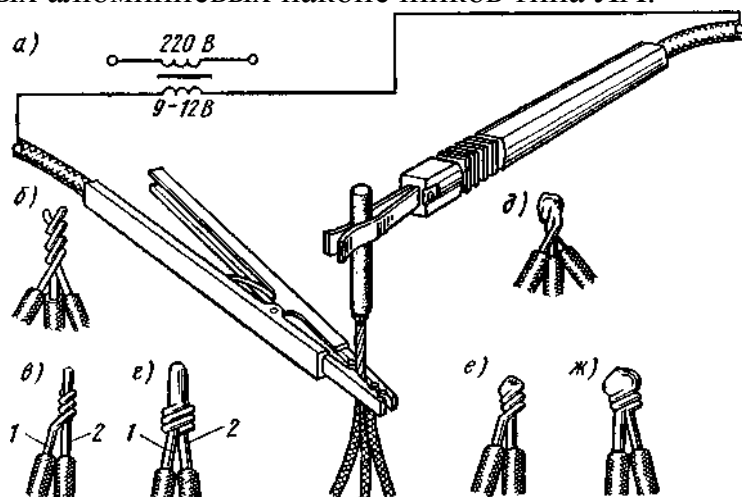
Электросварка угольным электродом: *а* – процесс сварки; *б* – алюминиевые жилы, подготовленные к соединению; *в*, *г* – алюминиевая 1 и медная 2 жилы, подготовленные к соединению; *д* – сварное соединение алюминиевых жил; *е*, *ж* – сварное соединение алюминиевой и медной жил
